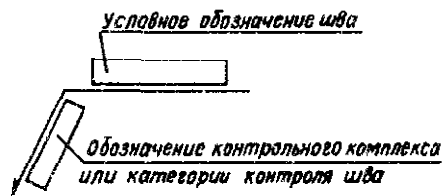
Указание обозначения категории контроля сварного шва
